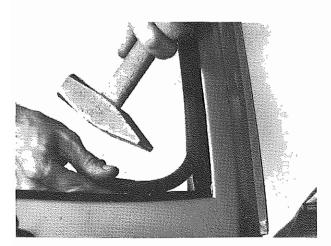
Montare guarnizione "Guistall" Assemble "Guistall" gasket
